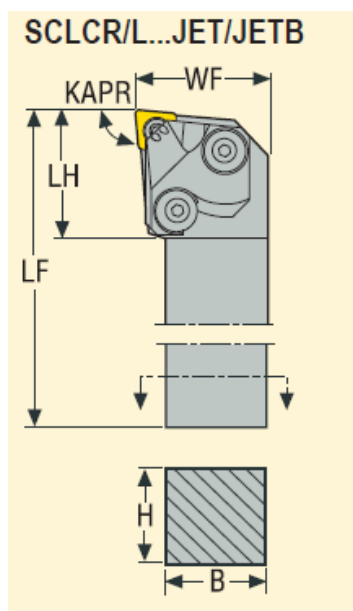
Державка резца для черновой обработки вала К-12-11
